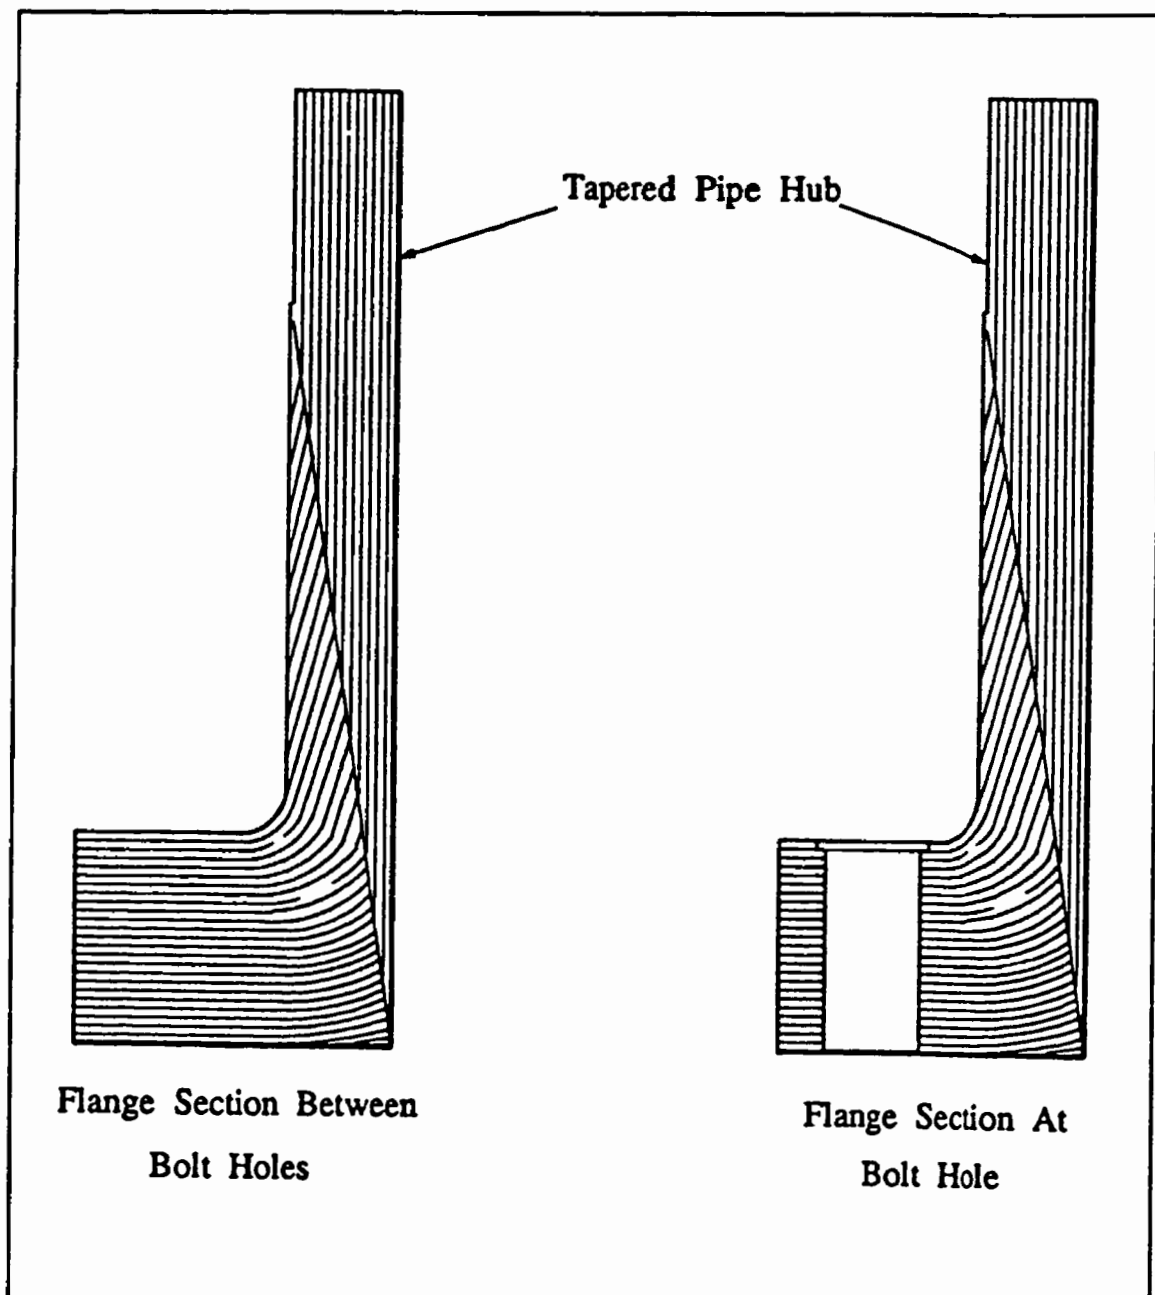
Bride en deux pièces moulée sur un tuyau de section trapézoïdale (Sun 1995)
